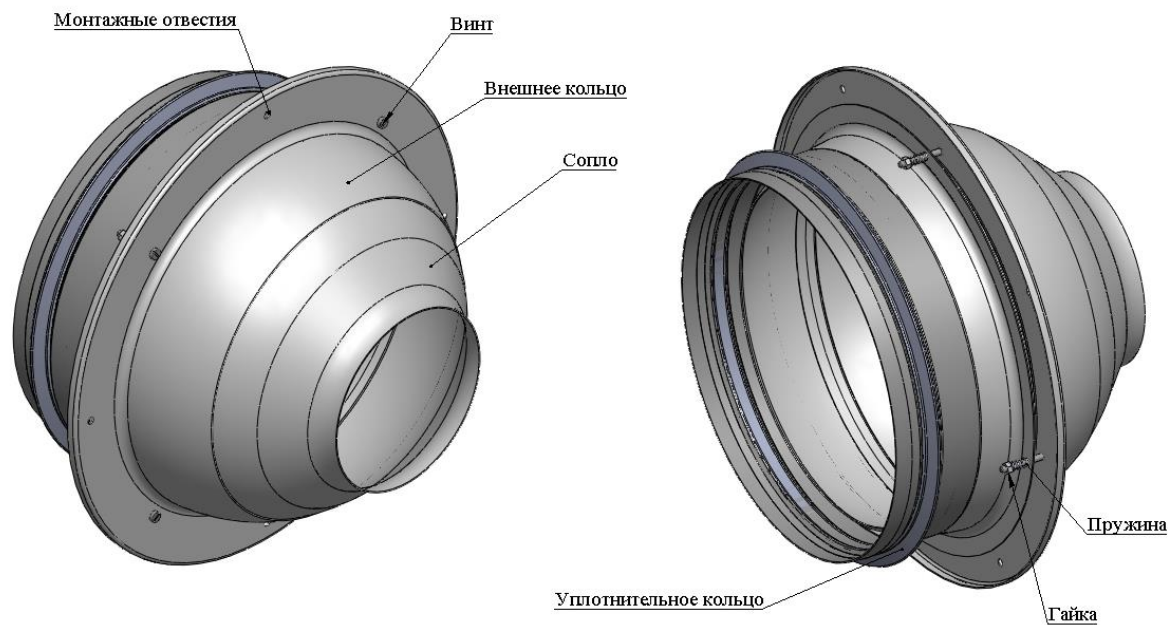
Внешний вид и конструктивные элементы 3СДК.
